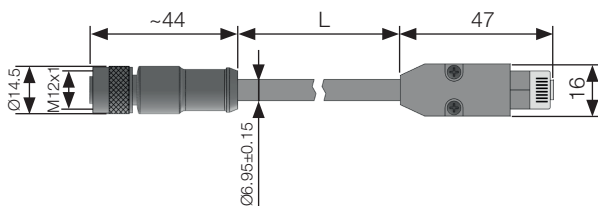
Verbindungskabel mit DRIVE-CLiQ/S115-Stecker, Beispiel
